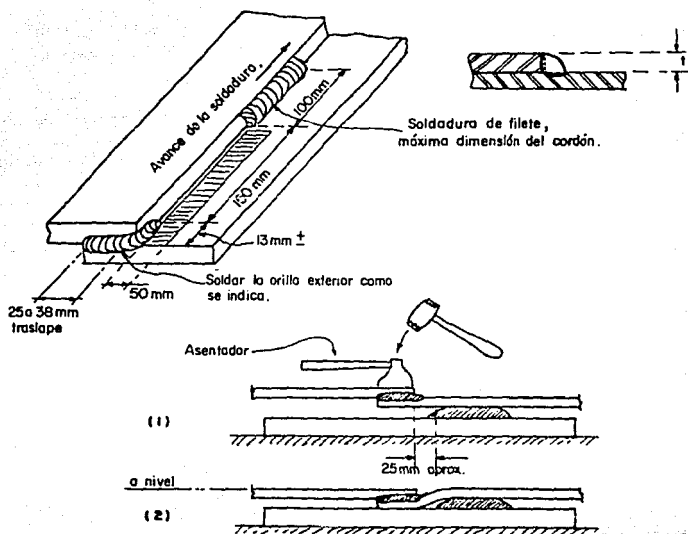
Soldadura del cordón exterior en forma de Filete.
